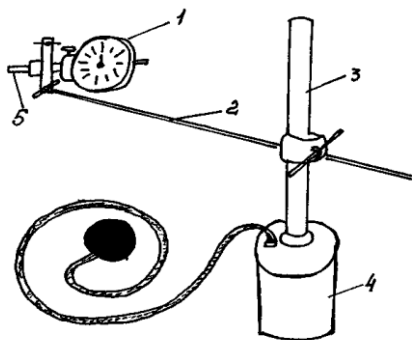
Приспособление КИ-4850 ГОСНИТИ для измерения зазоров в подшипниках
